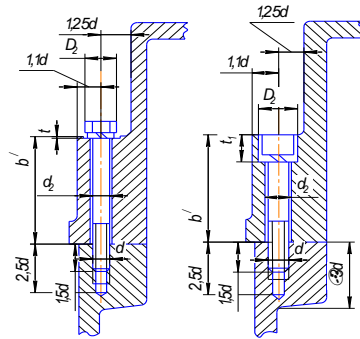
З'єднання кришки з корпусом: а – болтами з зовнішньою шестигранною зменшеною головкою; б – гвинтами з циліндричною головкою і внутрішнім шестигранником
